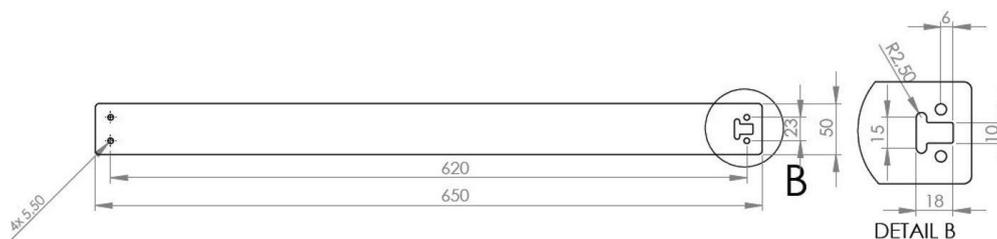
Placa de reforço de suporte de parede do teclado 600
